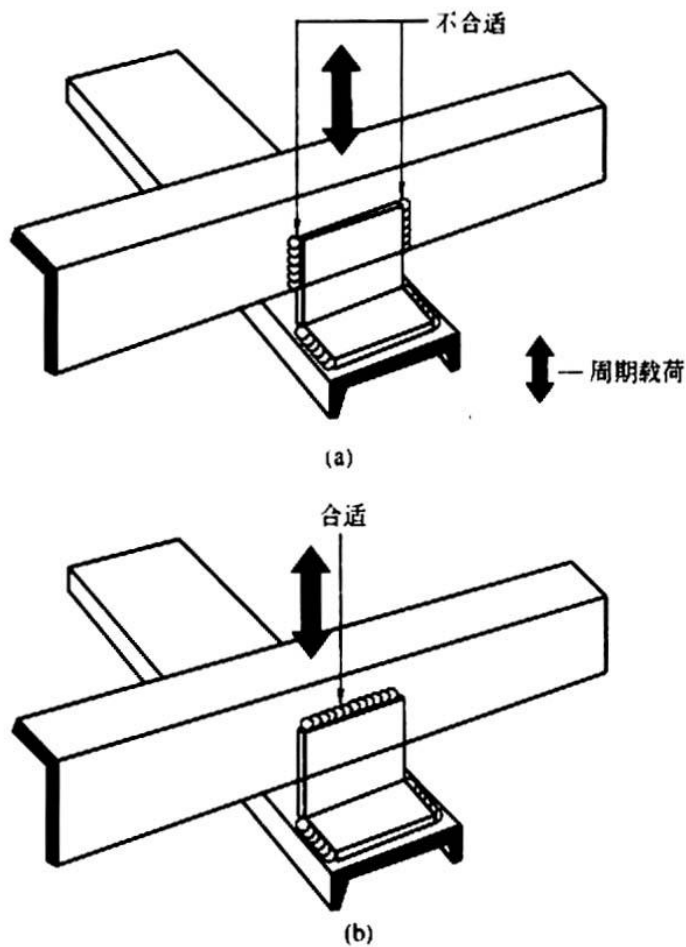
用沿中轴线的一条焊缝代替两条剪切焊缝
